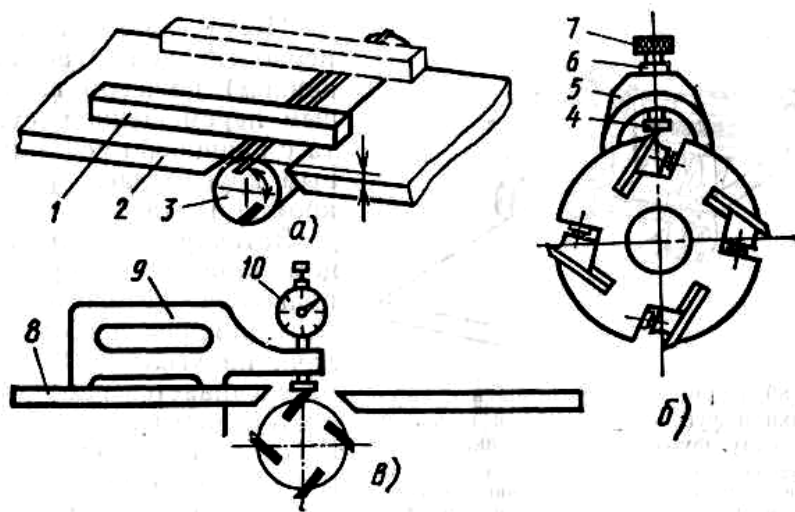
Выверка ножей в ножевом валу фуговального станка:
